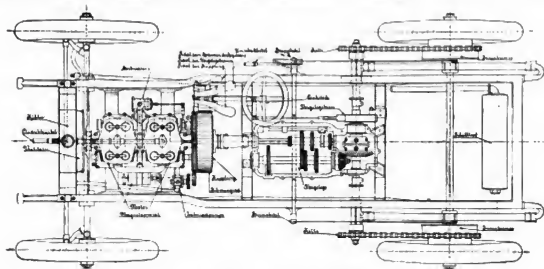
Vieroyl, Benzwagen, Grundriss.
